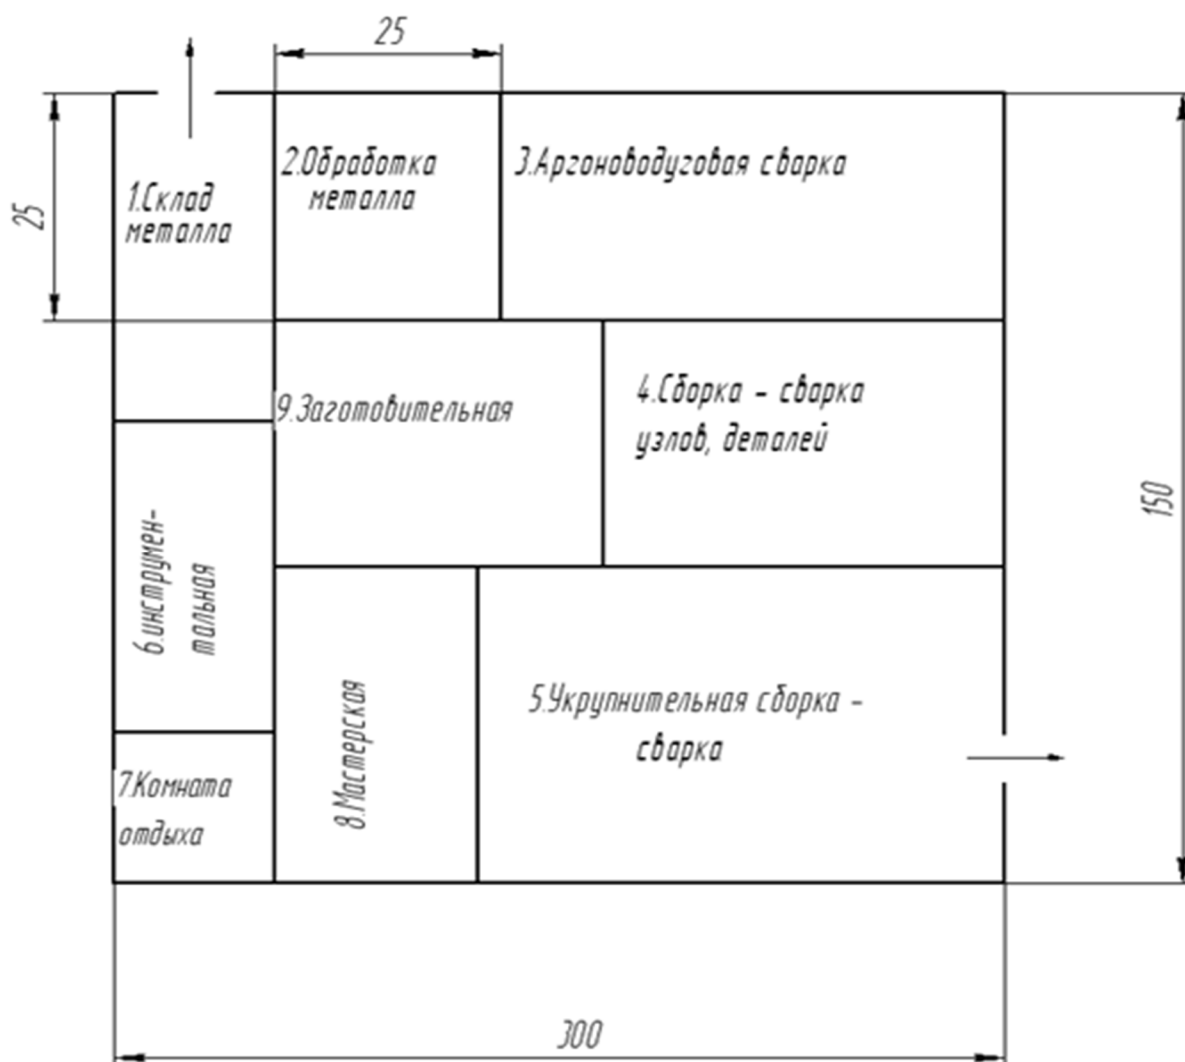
Описание схемы помещения в сварочном цехе
